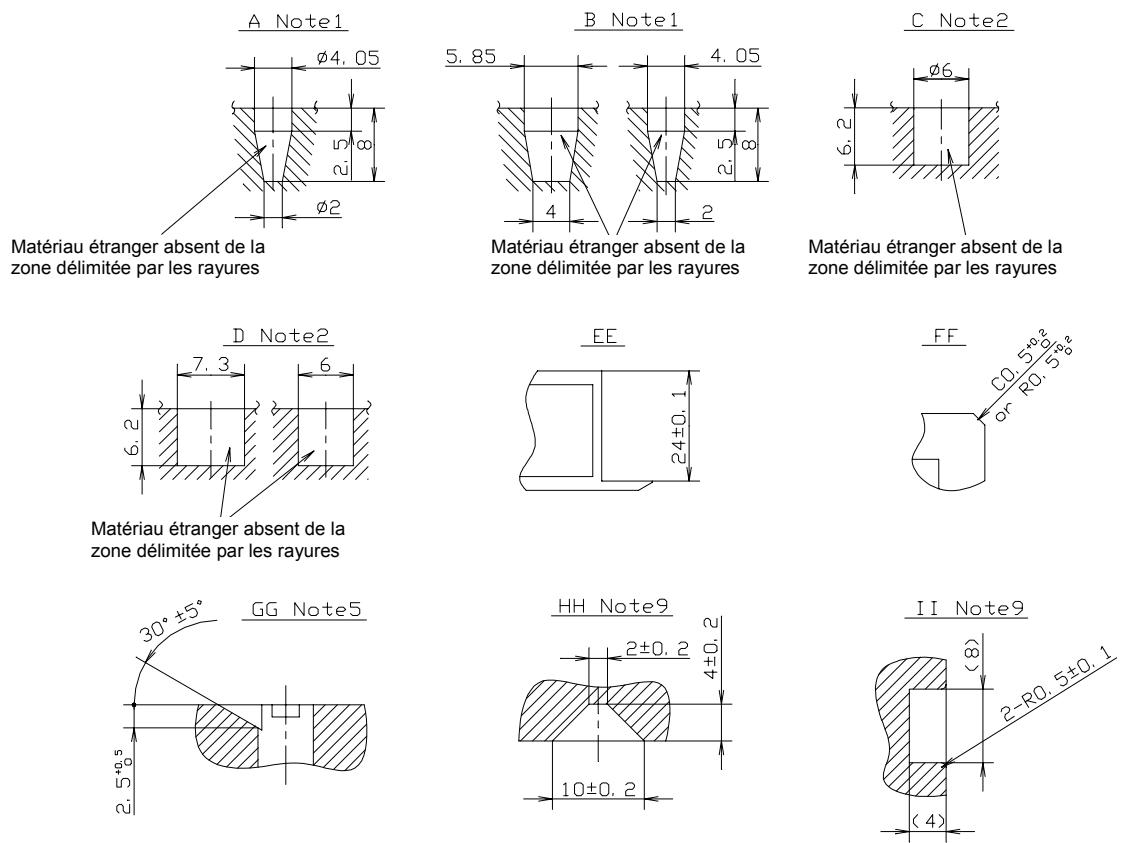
Dimensions – Vue de dessous et latérale de la cassette (1)
